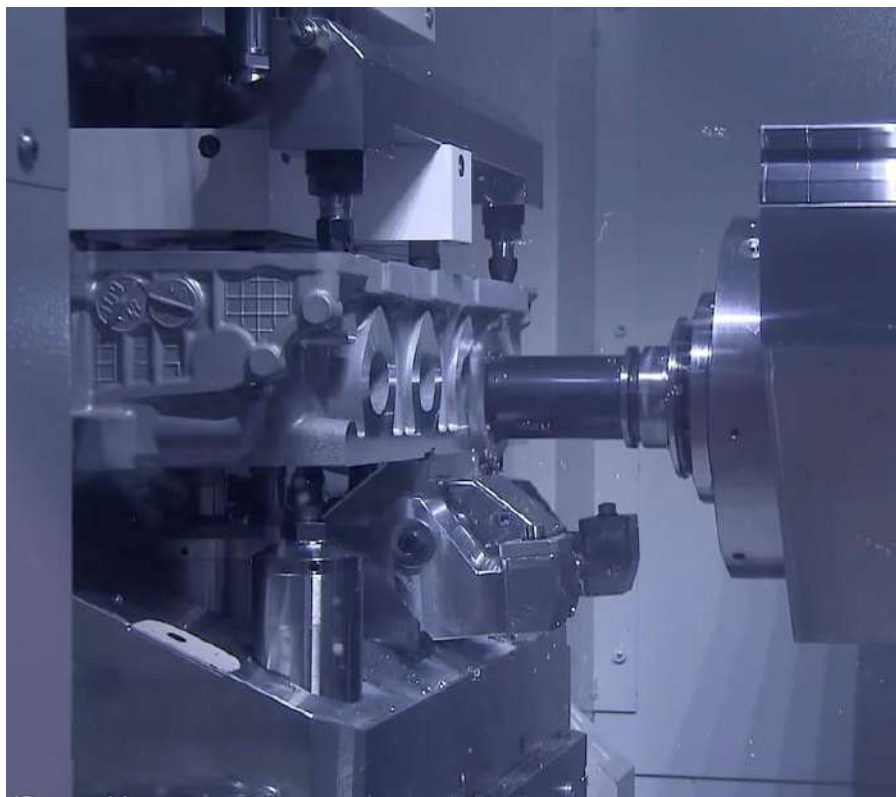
Процес фрезерування отворів головки блока на верстаті з ЧПУ
